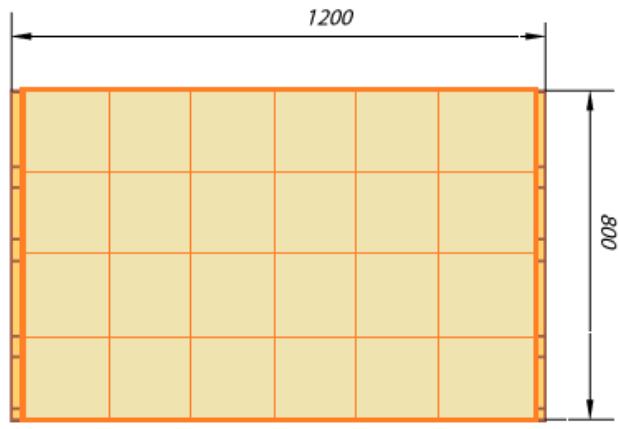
Схема размещения оборудования на паллете (вид сверху)
